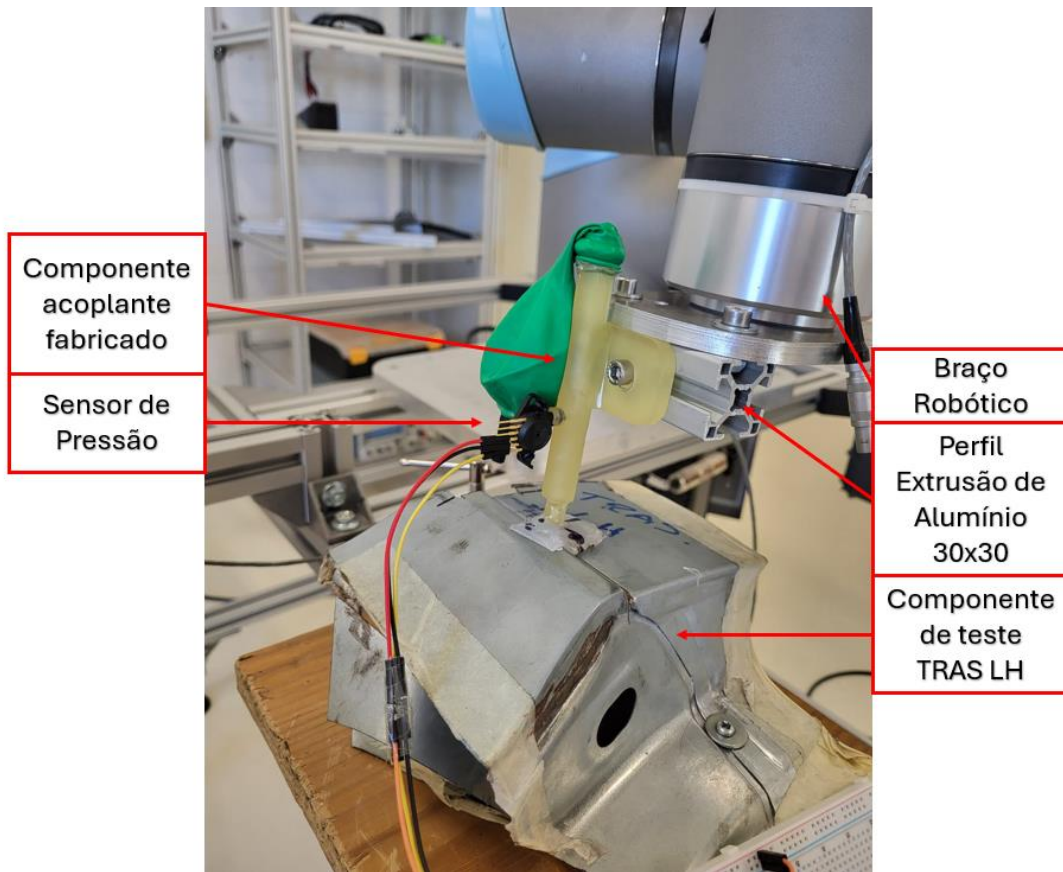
Montagem do componente acoplante fabricado ao robô
